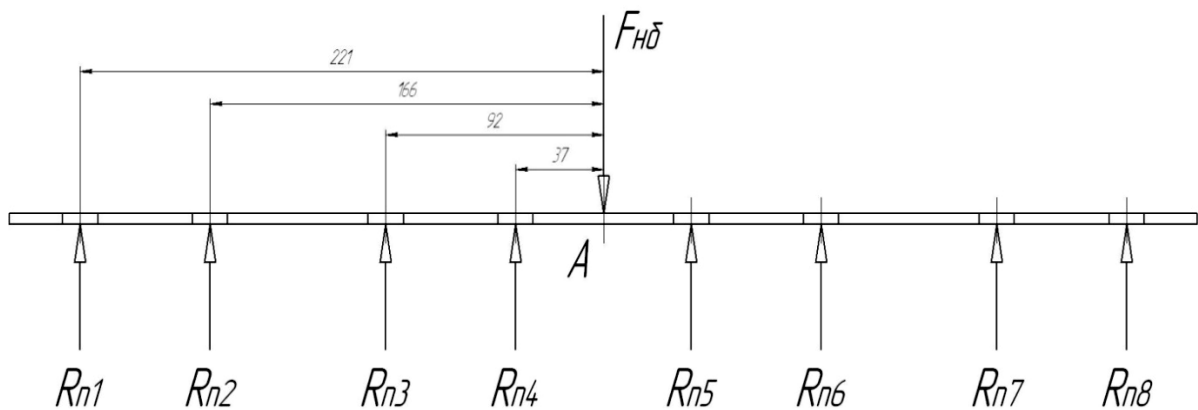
Пристрій для одночасного стискання клапанних пружин.
